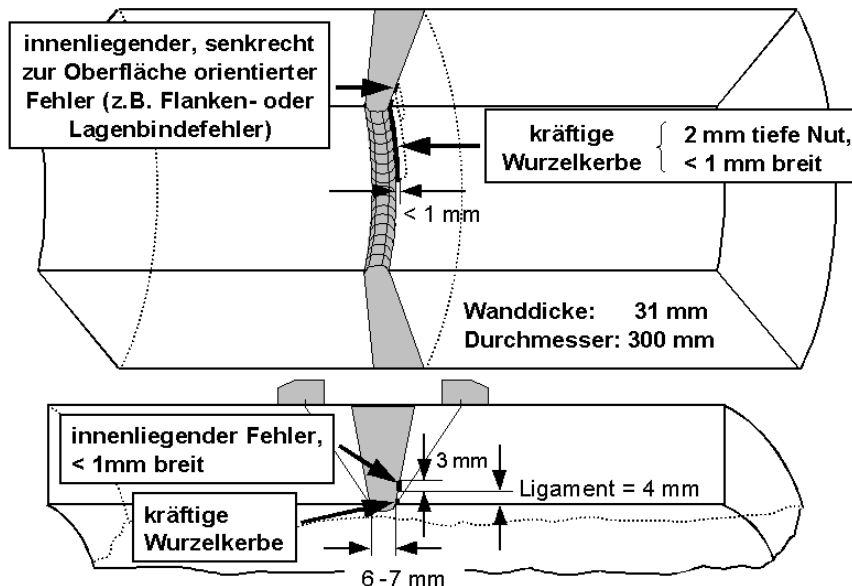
Rohrförmiger Testkörper für die Schweißnahtprüfung
